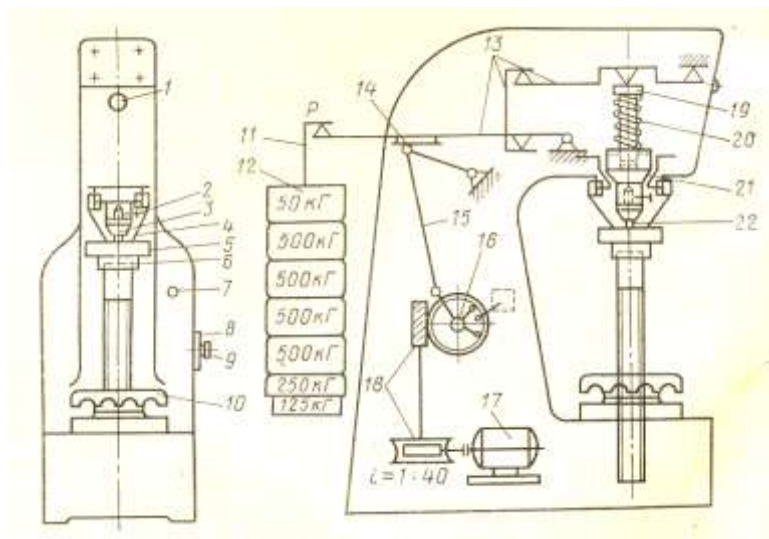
Схема устройства твердомера ТШ (прибор Бринелля)
